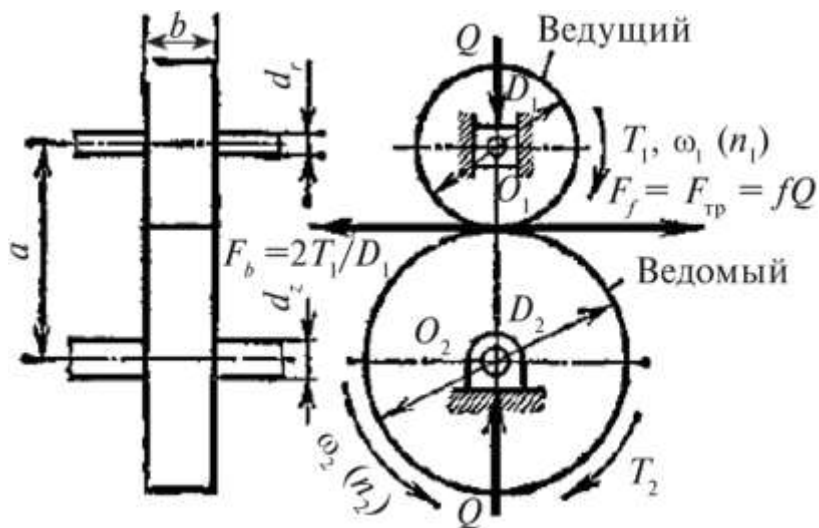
Схема цилиндрической передачи с гладкими катками
